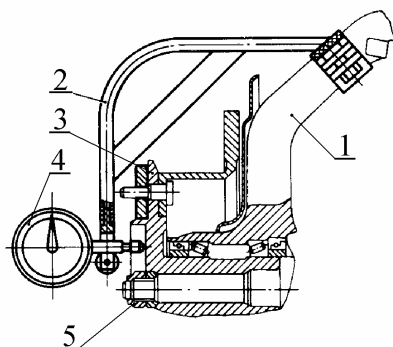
Замер осевого зазора в подшипниках ступицы переднего колеса полноприводного автомобиля:
